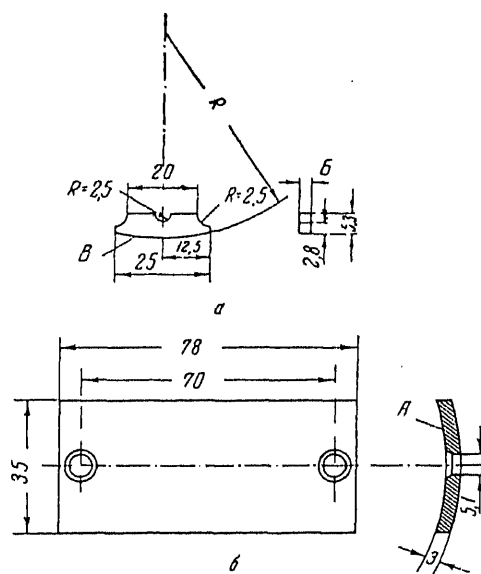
Образец для испытания на износ к машине трения 77 МТ-1. Поверхности А, Б, В не обрабатываются
